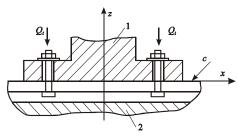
Сопряжение "подошва корпуса – стол станка"
